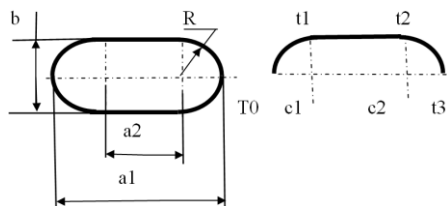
Шпоночный участок вала с нанесением размеров и его кодировочная схема
